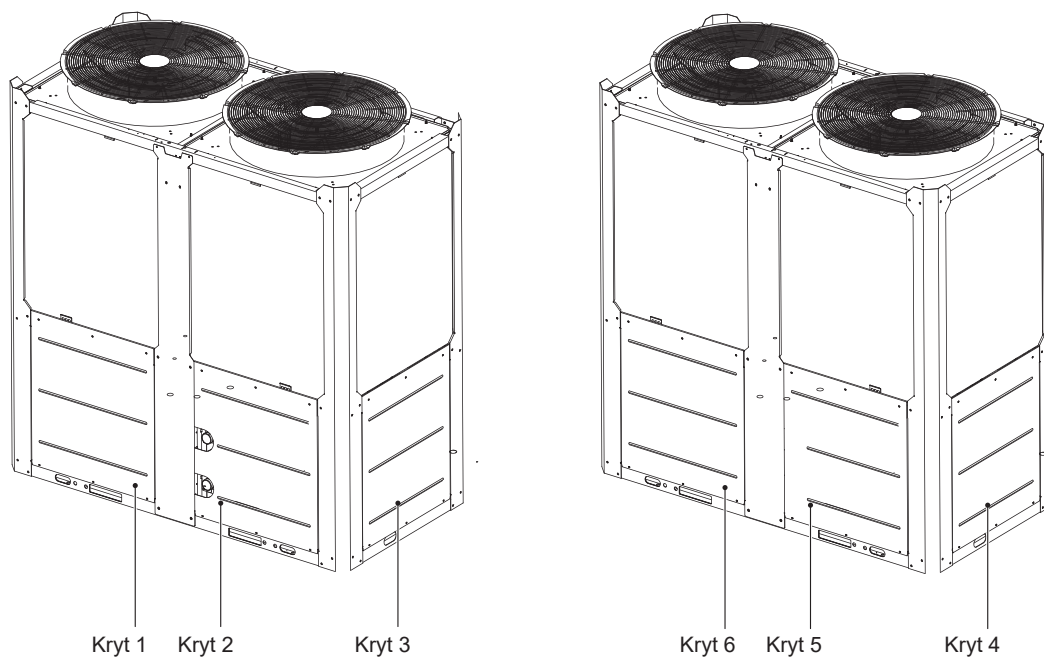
Dvierka 50KW, 65KW, 75 KW
